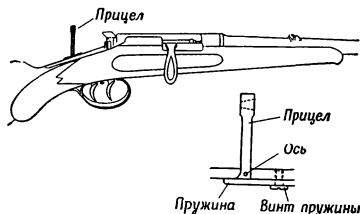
Простейший кольцевой прицел, установленный на охотничий карабин, и детали его устройства
